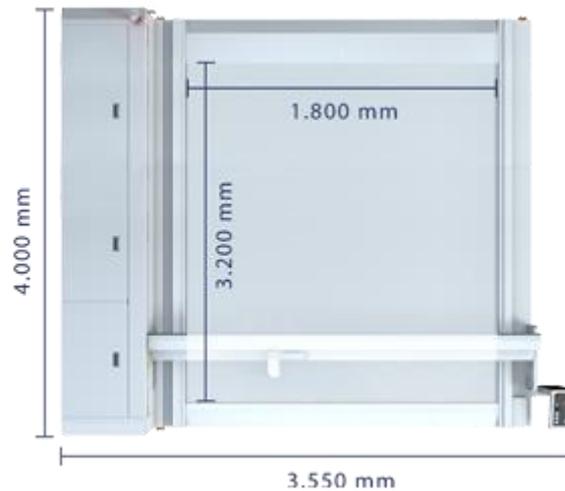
Dimensiones Cortadora láser. Fuente: www.eurolaser.com
